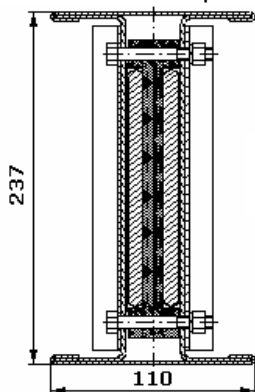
Поперечное сечение шинопровода на ток 1600А.
